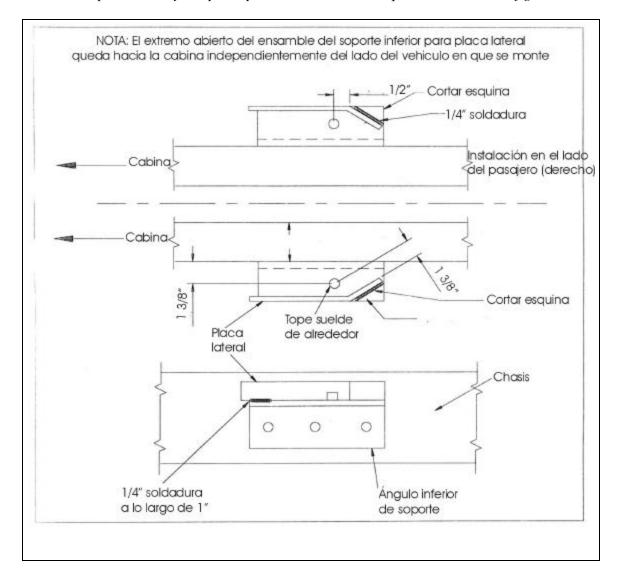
Posiciones del ángulo inferior de soporte y del tope.
